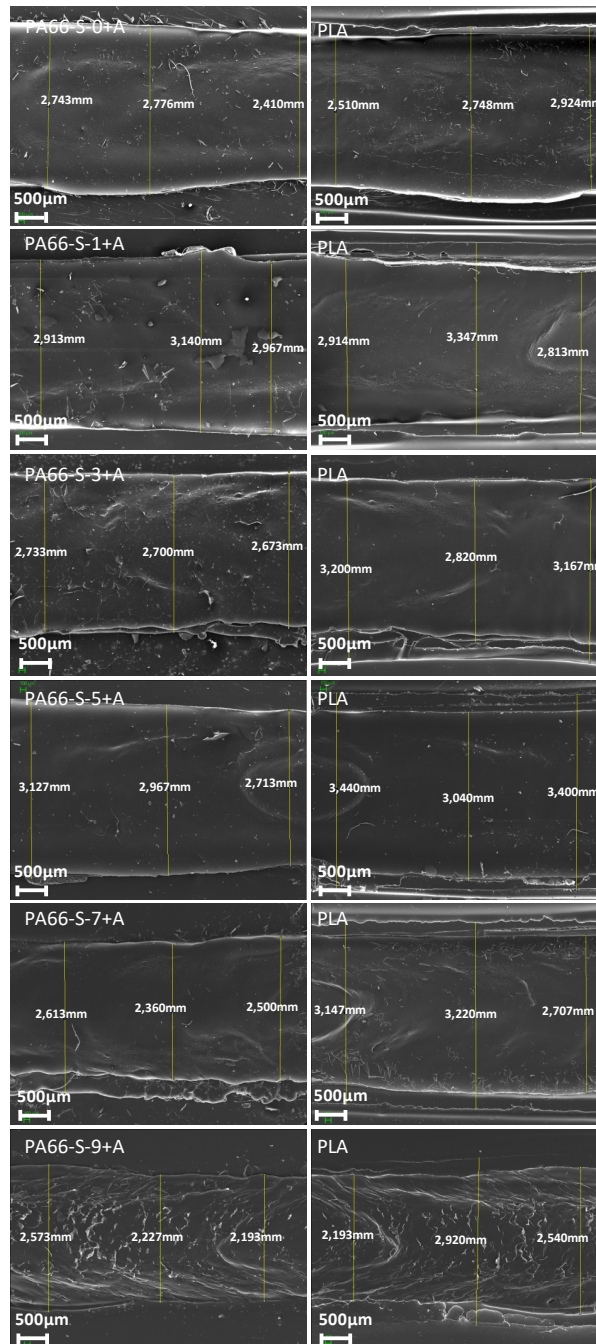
Determinación del cordón de soldadura de las soldaduras en los sistemas PLA/PA66 ensayados de despegado.
